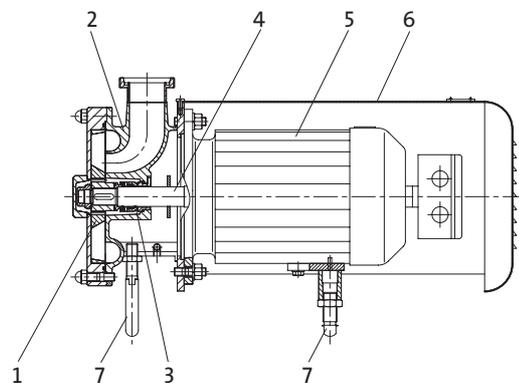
Secțiune transversală pentru SIPLA Bloc-SUPER pe picioare cu bilă din oțel inoxidabil
